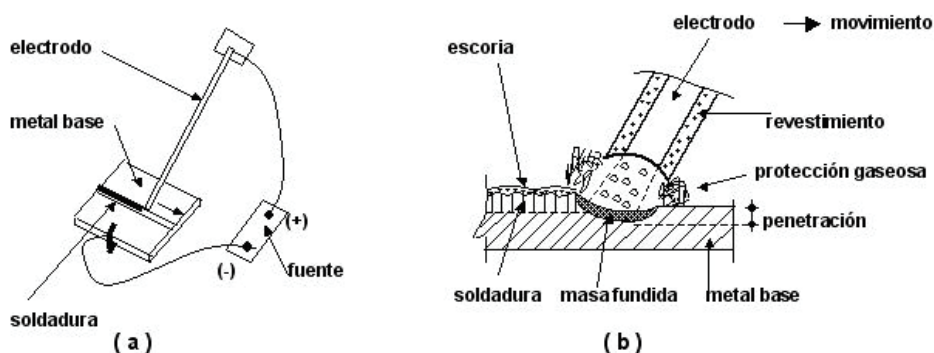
| Soldadura por arco eléctrico con aporte de material
